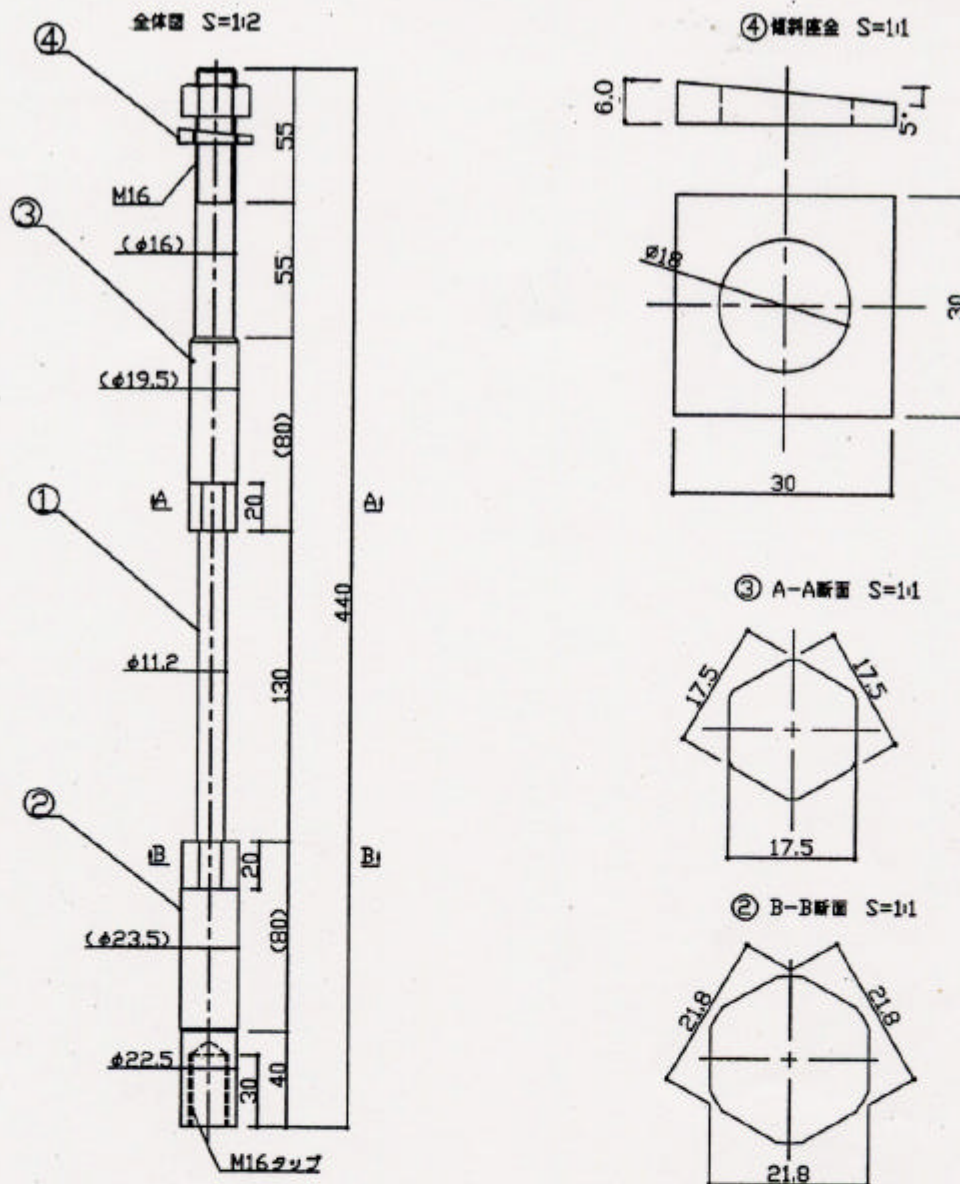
2 : 耐震Jケーブルの形状詳細 (mm)
